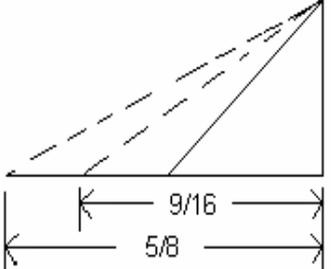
Requerimiento adicional de metal de soldadura por escasa preparación
